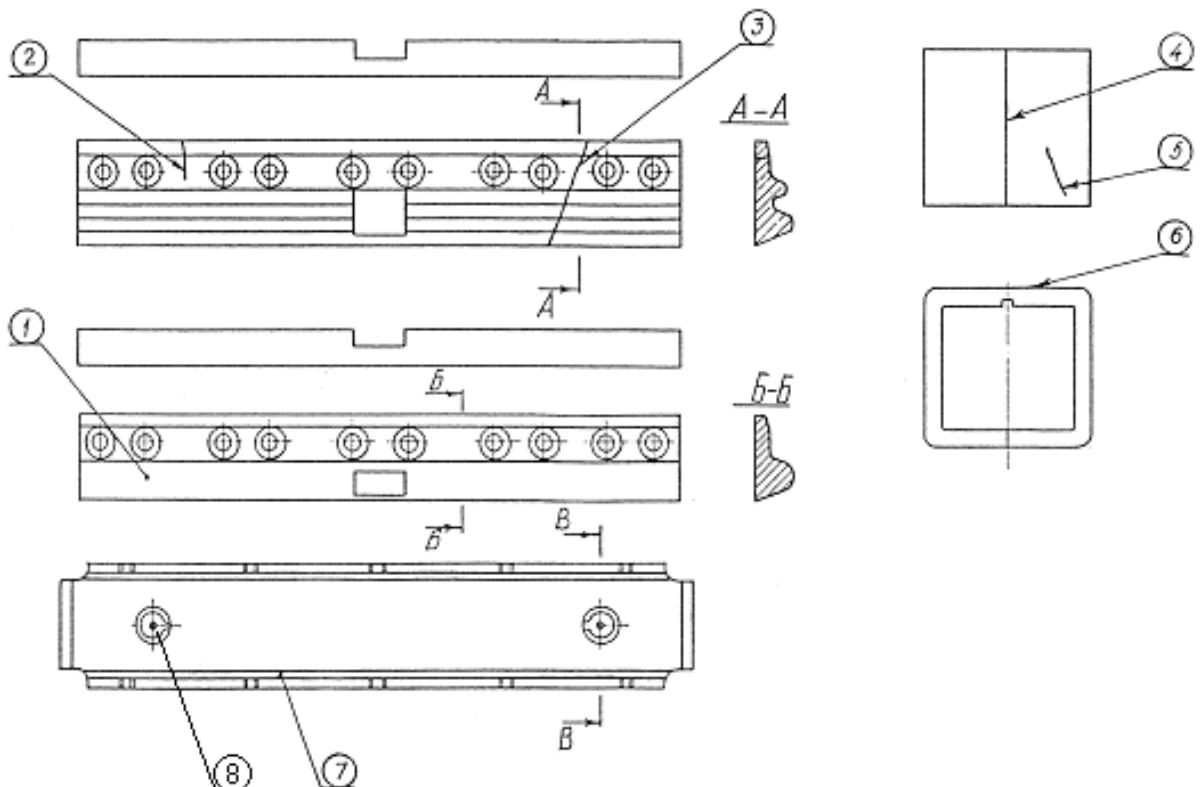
Основные дефекты деталей центрального рессорного подвешивания, ремонтируемые сваркой или наплавкой
